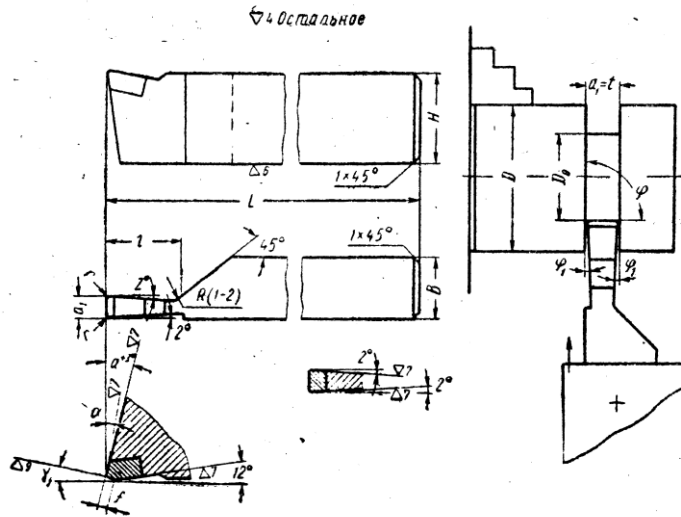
Токарный отрезной резец, оснащенный пластинкой
